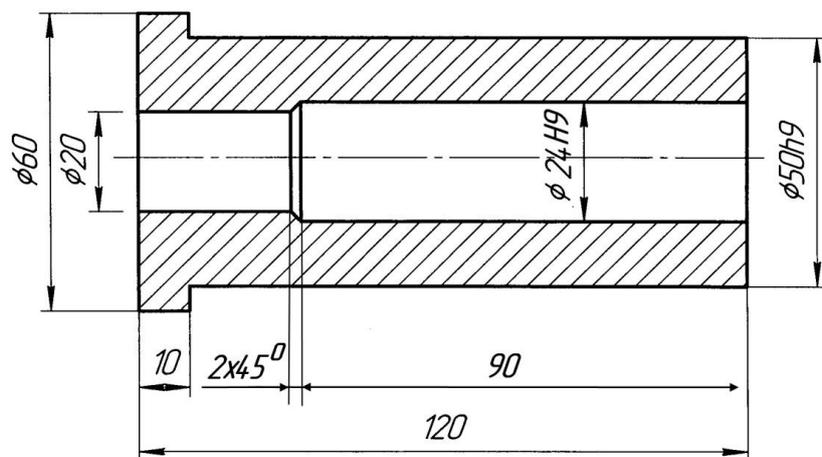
Эскиз детали «Вал полый», материал – сталь 35ХМА.
